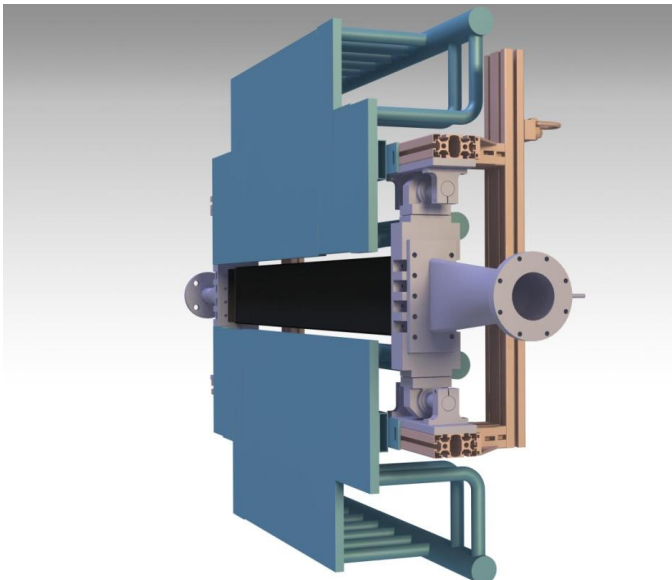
Dessin d'ensemble du montage module – face irradiée
